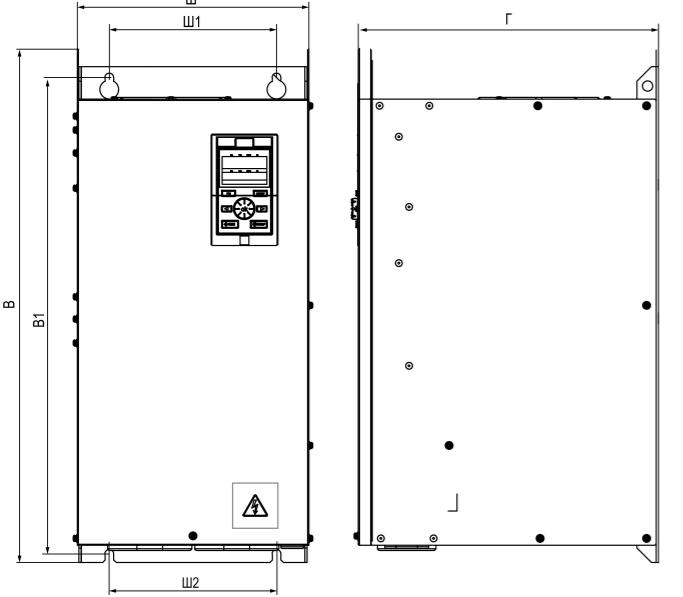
Габаритные размеры прибора в корпусе типоразмера 6
